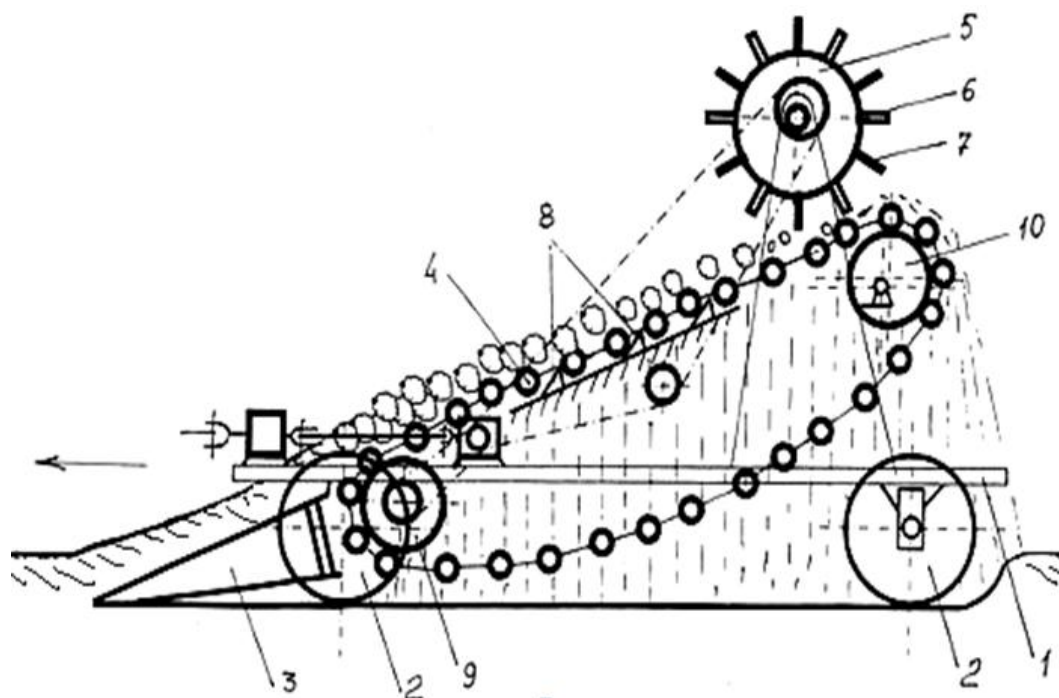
Технологическая схема машины для подготовки почвы перед посадкой картофеля: 1 – рама; 2 – опорное колесо; 3 – лемех; 4 – прутковый элеватор; 5 – комкоразрушающий колковый барабан; 6 – колки; 7 – планка; 8 – встряхиватель; 9 и 10 – ведомый и ведущий валы элеватора
